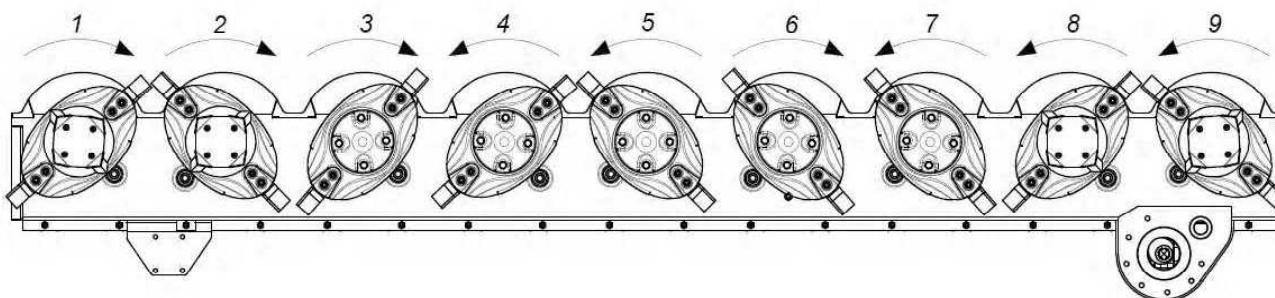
Направления вращения дисков режущего бруса косилки KDF 390.
